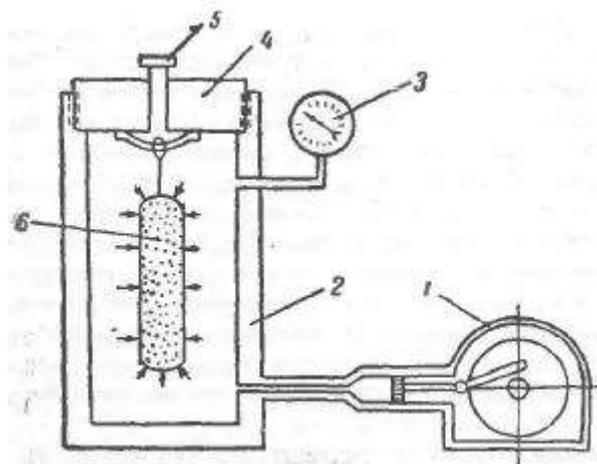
Схема установки гидростатического прессования: 1- насос высокого давления, камера прессования, 2- камера, 3- манометр, 4- затвор, 5- воздушник, 6- прессовка
